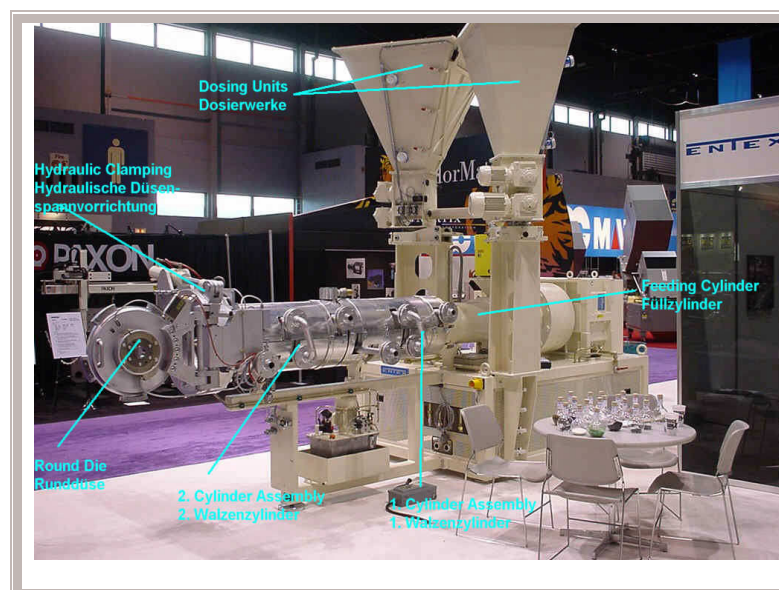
représentation du système de construction modulaire d'une extrudeuse à vis planétaires
